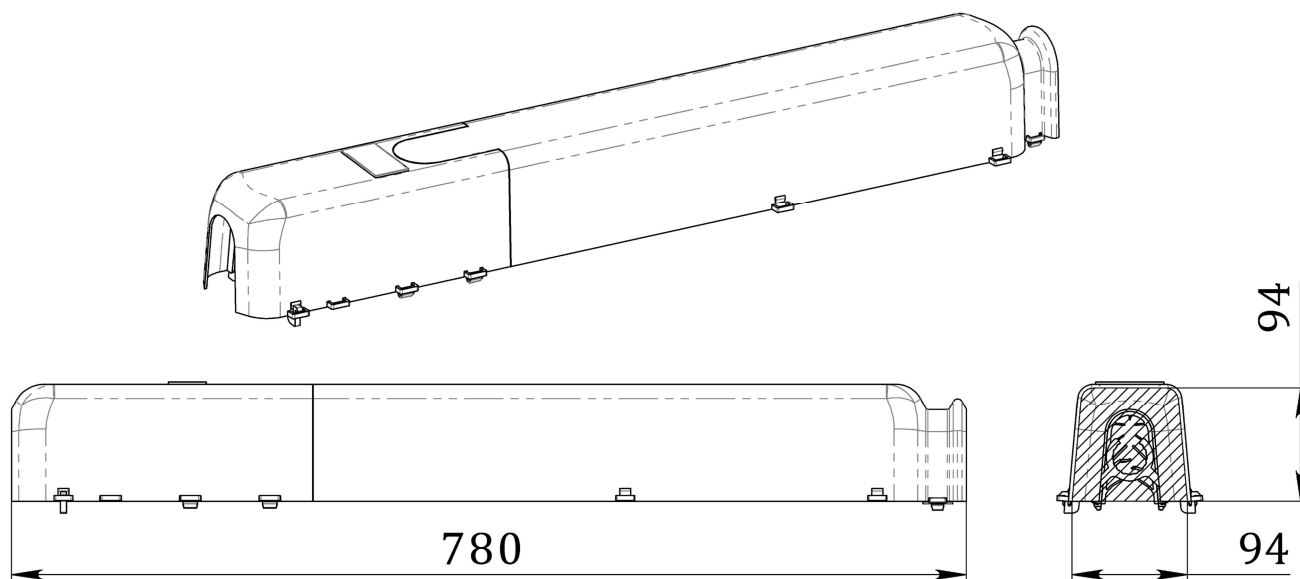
Общий вид и основные размеры ПЗУ-ВРА (сплошной кожух)
